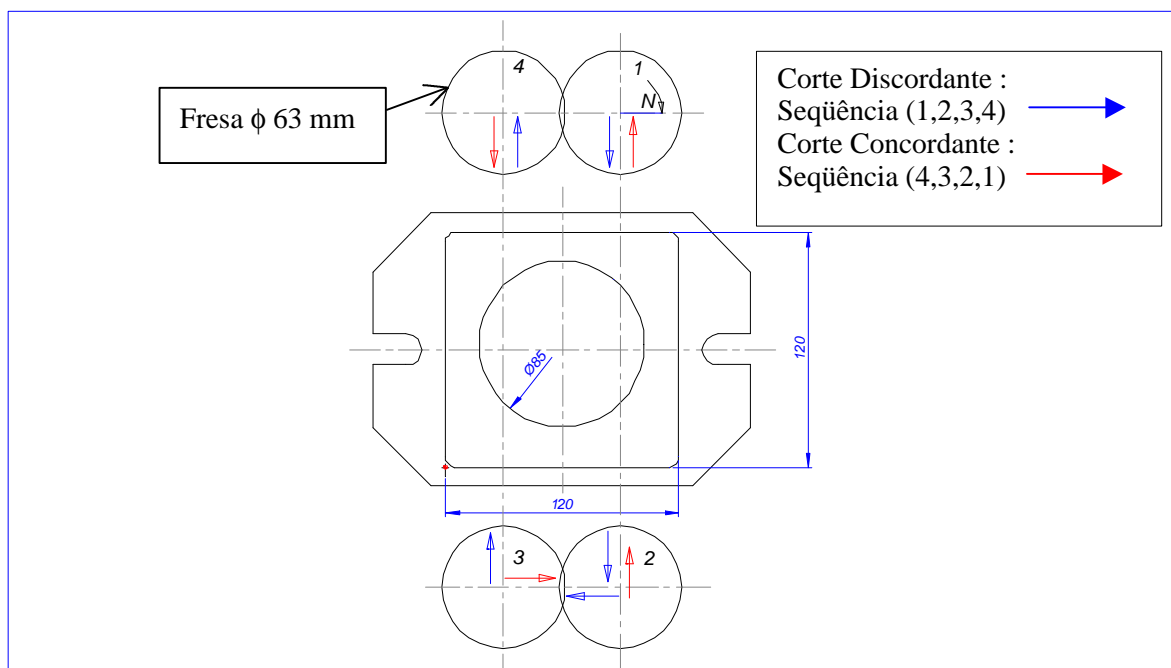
Usinagem da Superfície 2 nos sentidos concordante e discordante
